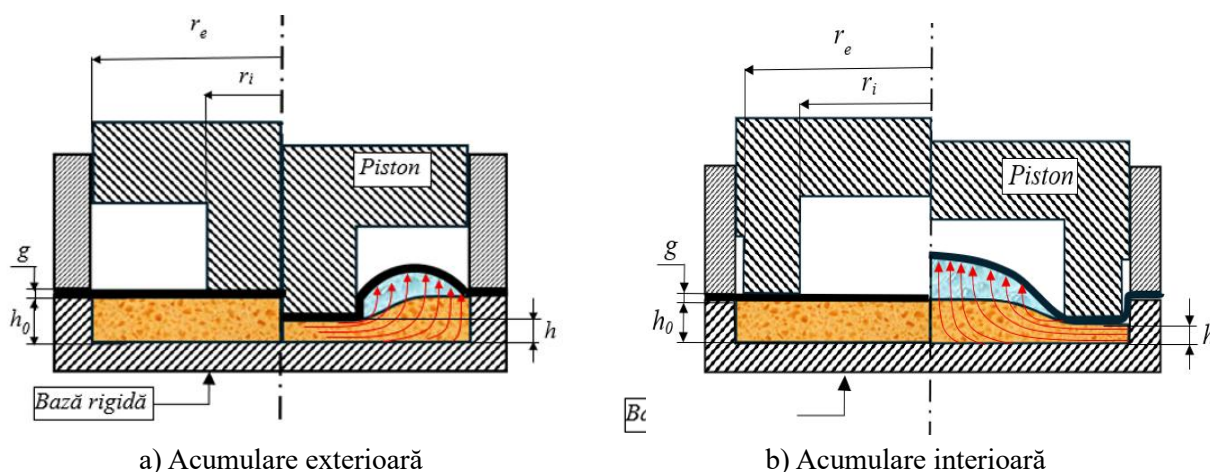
Schița de principiu a dispozitivului cu membrana plană cu două soluții constructive
